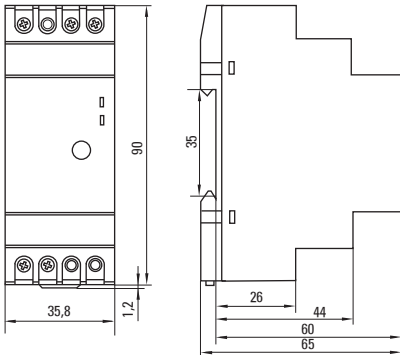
Габаритные размеры фотореле DIN-1 (ФР)
